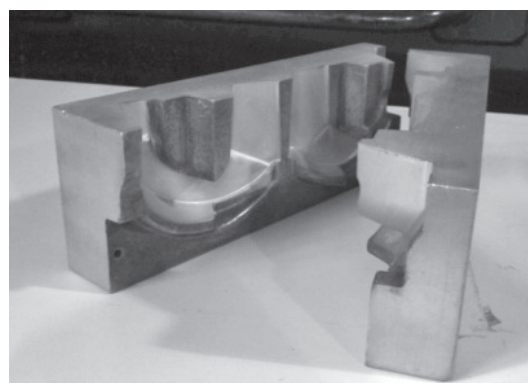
Стержевая оснастка для производства отливки «Колесо турбинное»
